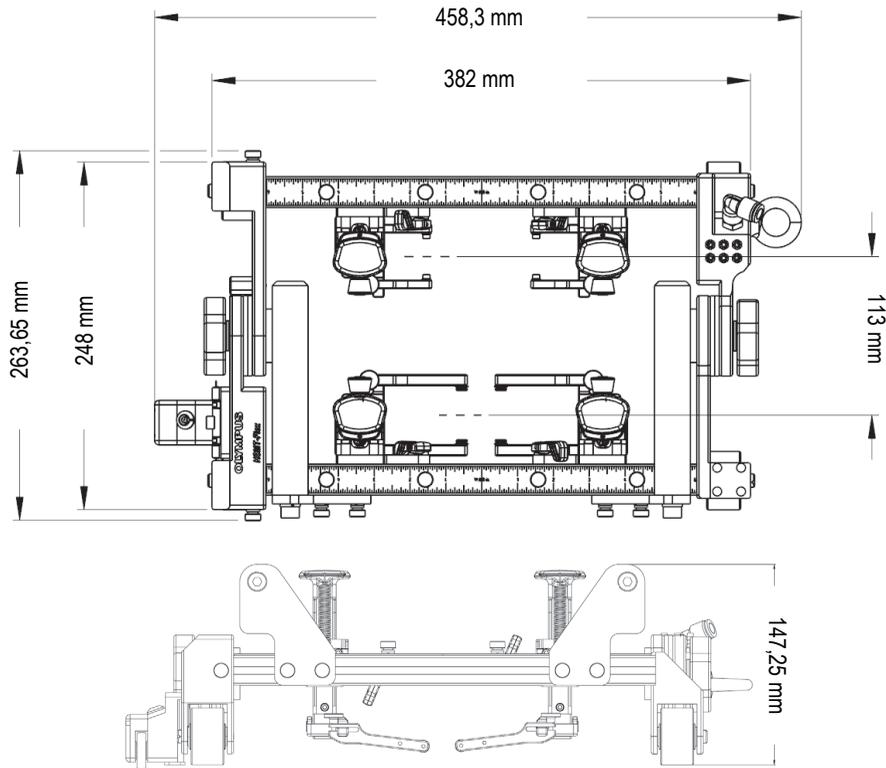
Dimensions du scanner — Vues de dessus et de côté
